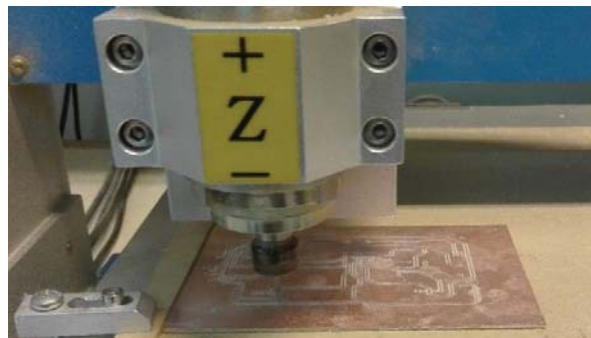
Perfilado de PCB en máquina CNC RS-3020.
